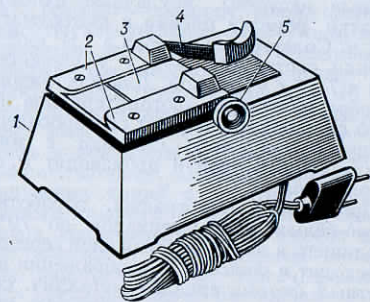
Резак для диапозитивов: 1 — корпус; 2 — направляющая рамка с пазами; 3 — кадровое окно; 4 — нож; 5 — рукоятка для перемещения плёнки.
